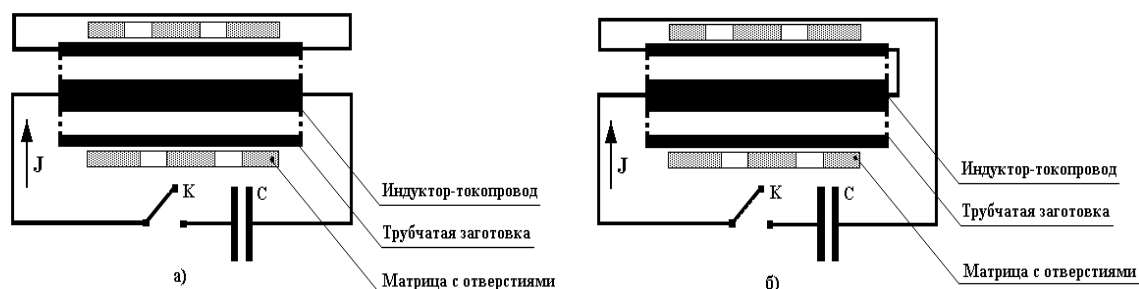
Принципиальные схемы «раздачи» полый цилиндрической заготовки, 1 – внутренний токопровод; 2 – полый цилиндр, подлежащий обработке.
